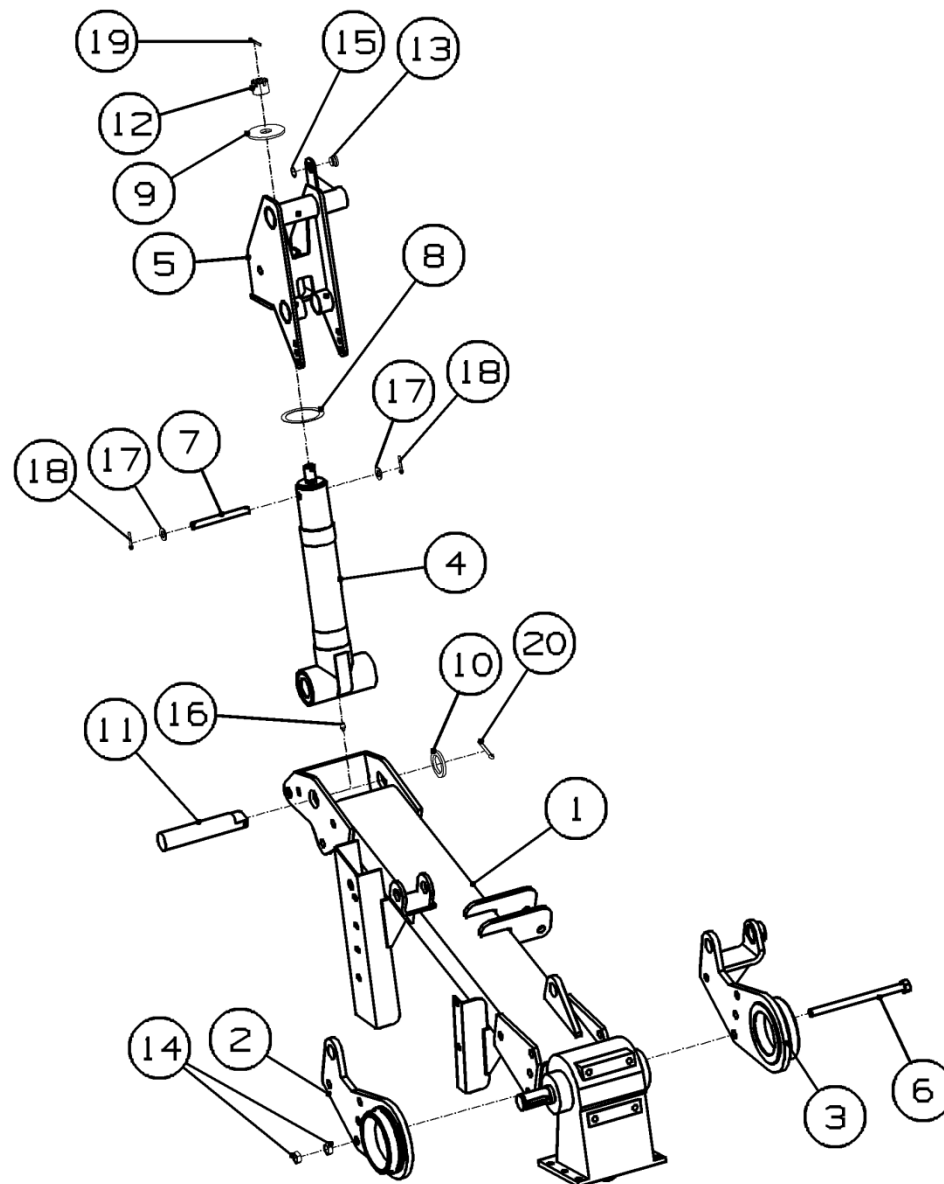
КРК-2.4.02.000А Установка бруса малого
